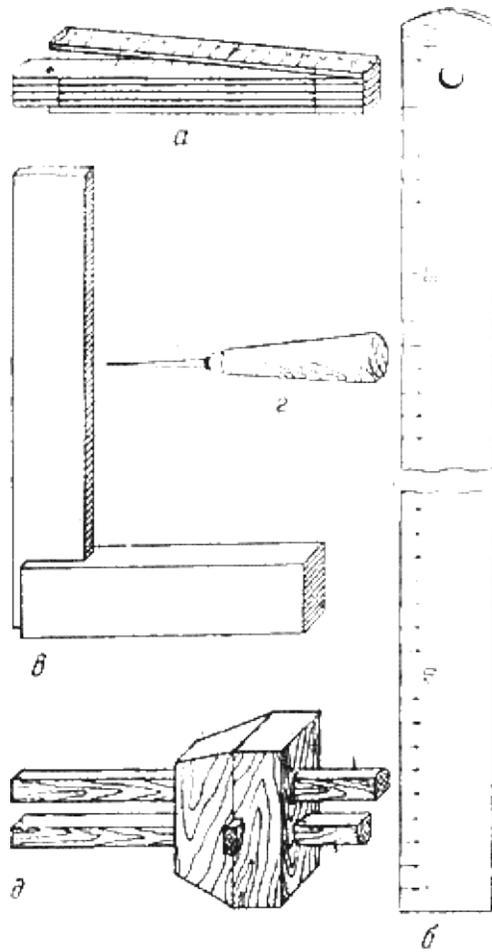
Разметочные инструменты: а — складной метр; б — метровая линейка; в — угольник; г — шило; д — рейсмус
